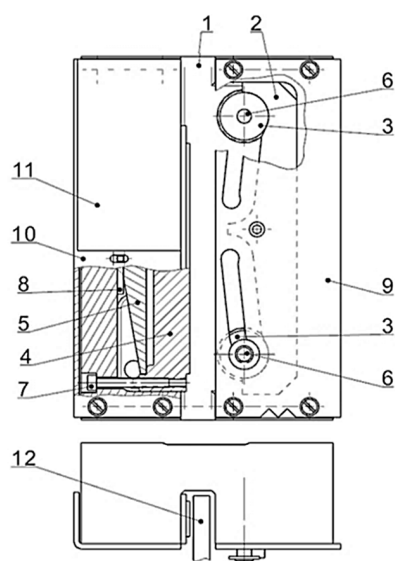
Общий вид ловителя плавного торможения двухстороннего действия производства ОАО «Могилевлифтмаш»: 1 – корпус; 2 – основание; 3 – ролики; 4 – тормозная колодка; 5 – пружина; 6 – оси; 7 – винты; 8 – регулировочные прокладки; 9 – направляющая пластина; 10 – пластина; 11 – табличка-пломба; 12 – направляющая лифта
